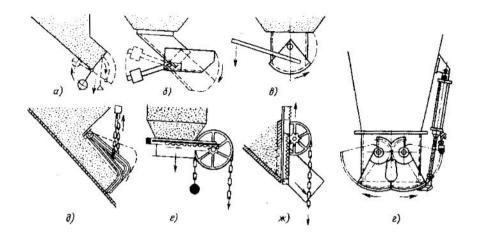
Затворы: а – клапанный откидной; б – клапанный подпорный; в – секторный: г – двухсекторный с пневматическим приводом; д – пальцевый;
